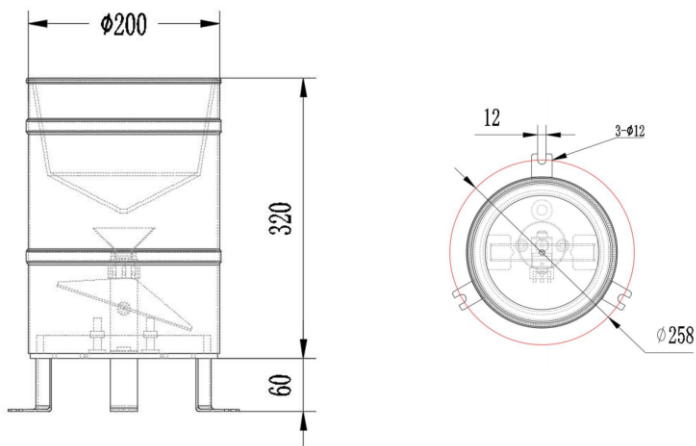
Размеры осадкомера с опрокидывающимся ковшом ИСВ400-07
